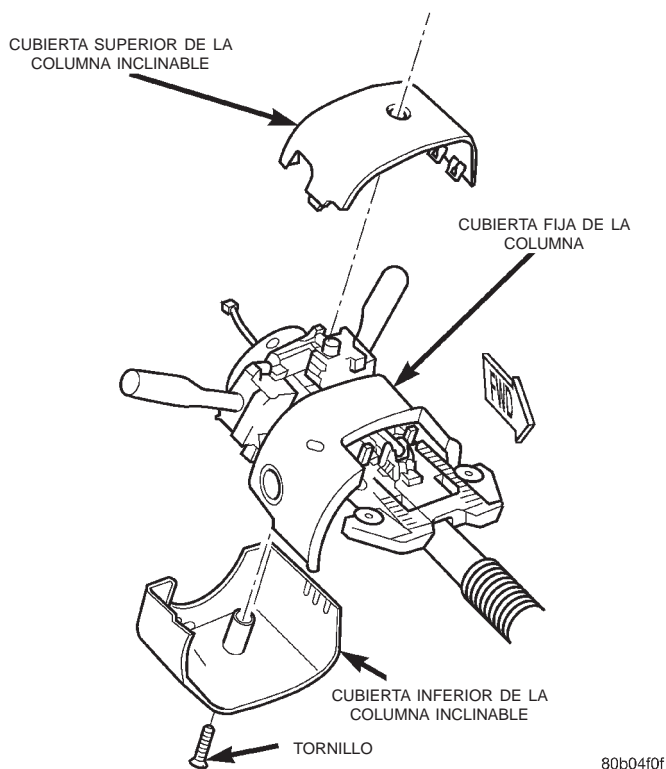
Desmontaje e instalación de las cubiertas de la columna de dirección
